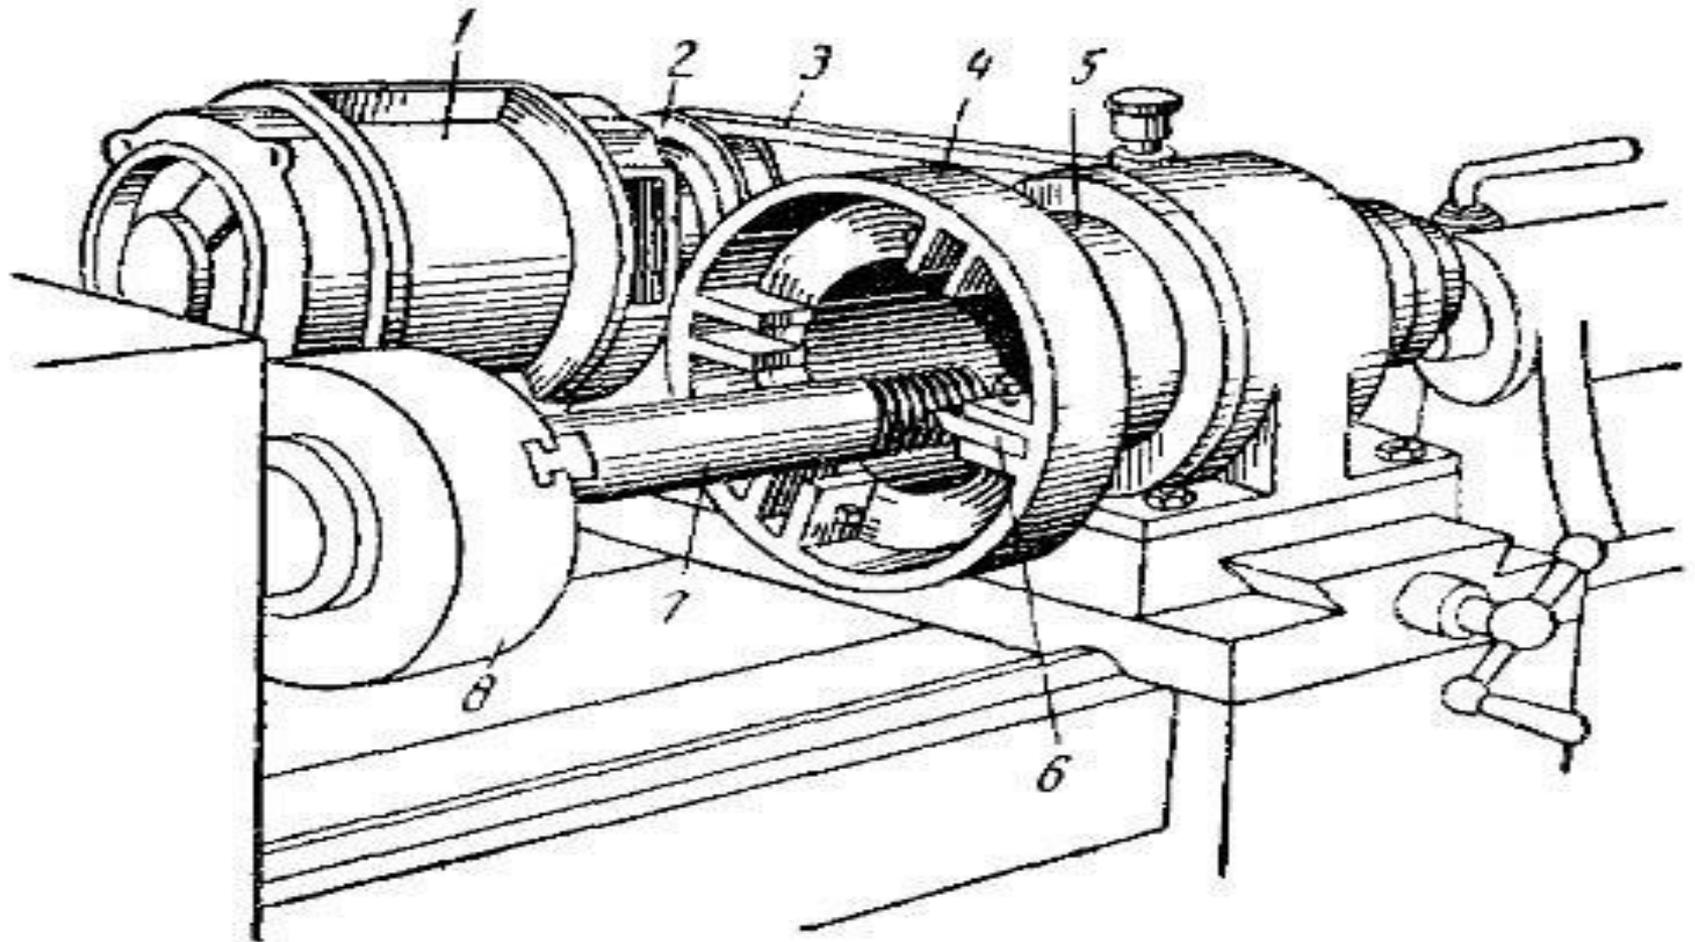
Приспособление для нарезания резьбы вращающимся резцом
